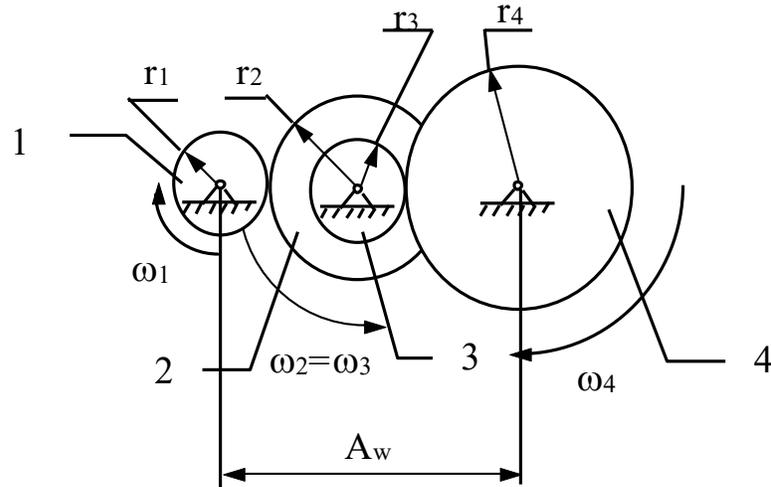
Кинематическая схема сложной зубчатой передачи с внешними зацеплениями
